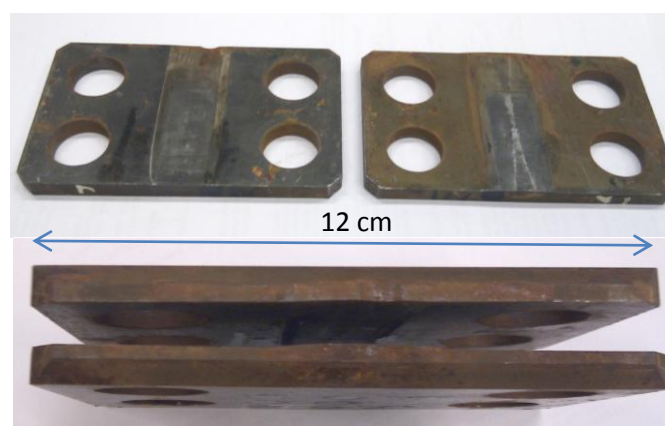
Mors spécifiques pour la machine de fatigue INSTON 1251
